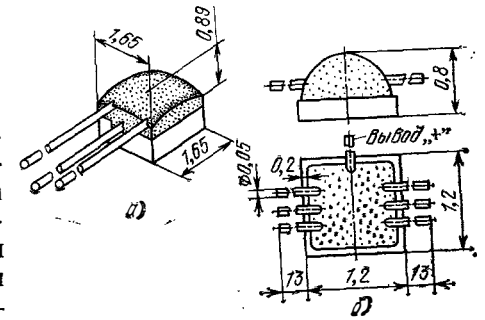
Конструкция бескорпусного транзистора (а) и диодной сборки (б) с проволочными выводами
